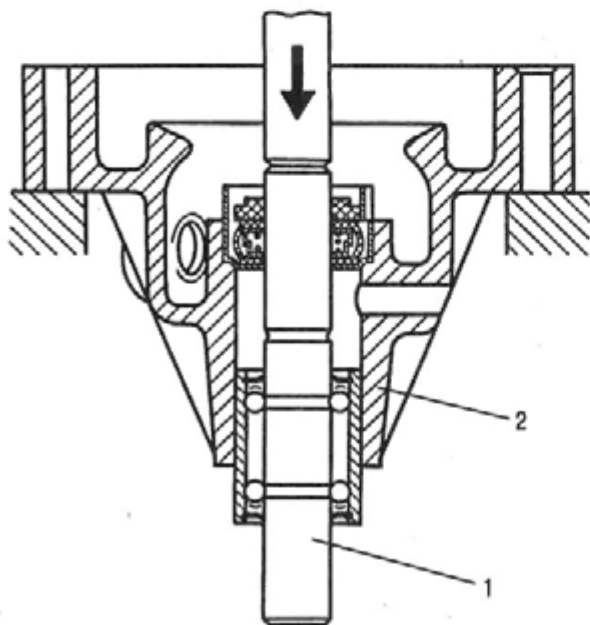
Выпрессовывание подшипника с валом водяного насоса:
